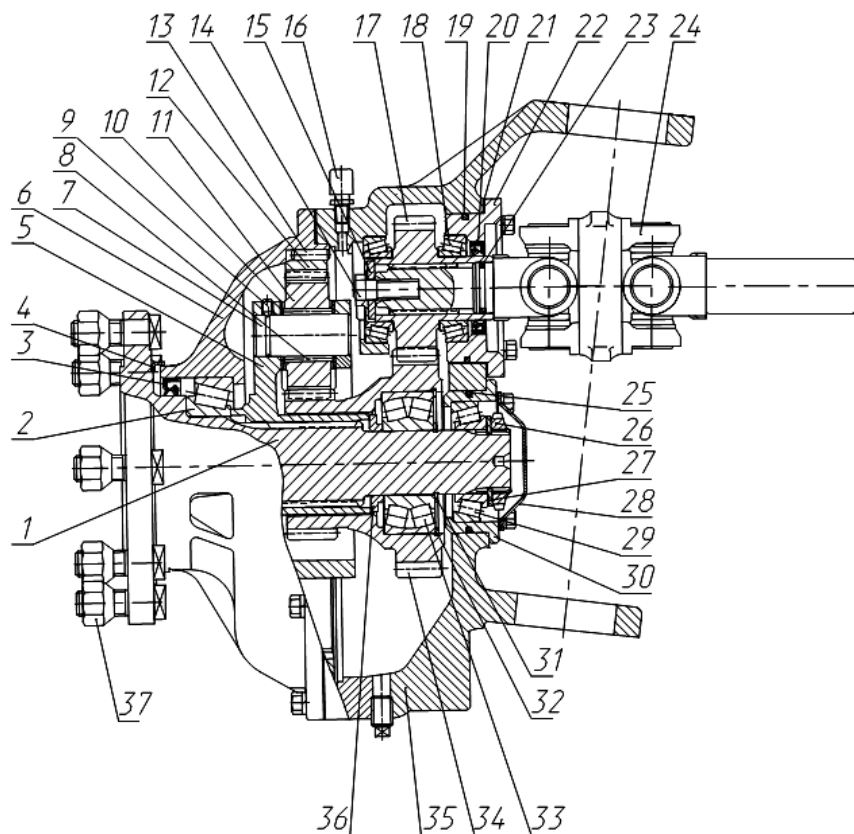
Колесный редуктор переднего ведущего моста трактора «Беларус-1523»:
